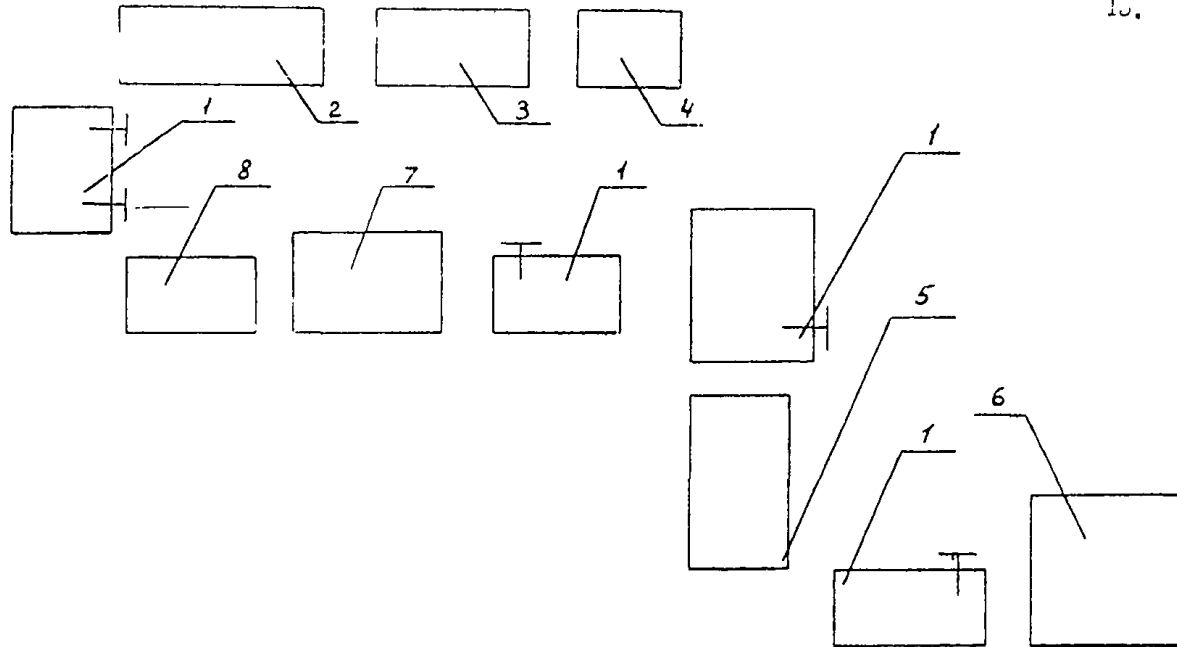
Типовая схема планировки рабочего места разборки и сборки узлов двигателя
